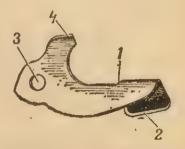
Затворная задержка: 1 — выступ; 2 — кнопка с насечкой; 3 — отверстие; 4 отражатель
